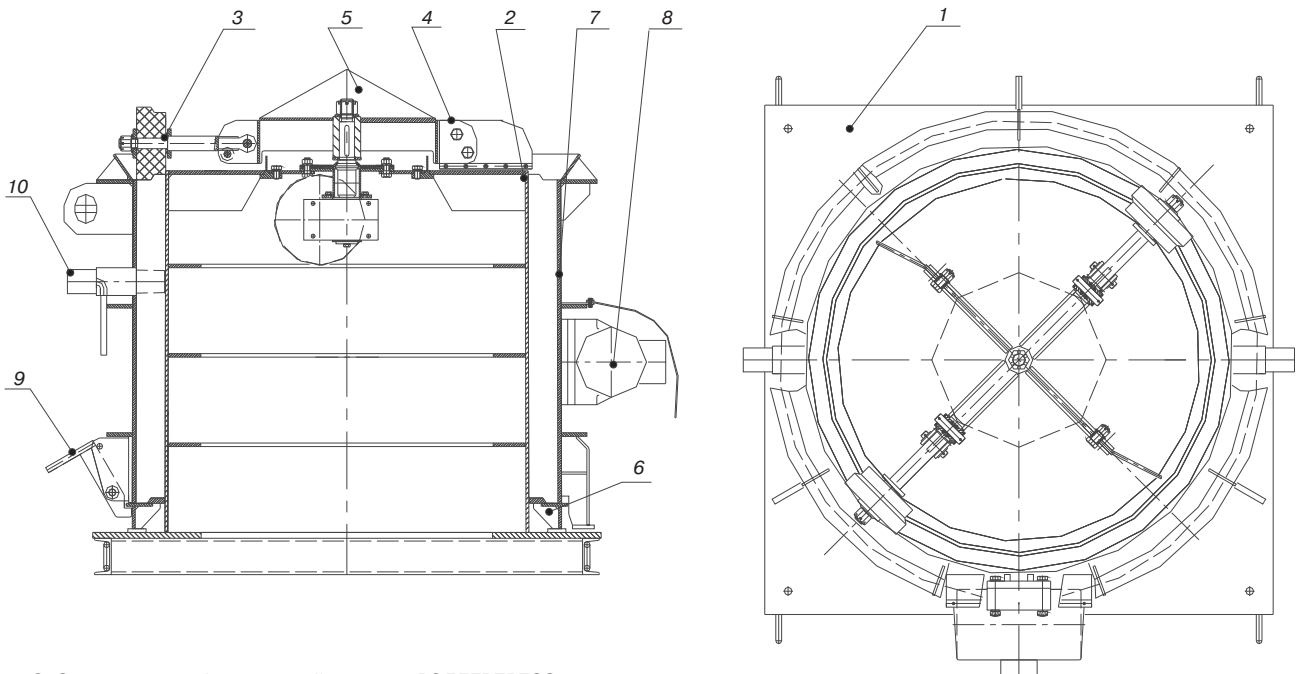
Схема роторно-формовочной машины «РОЛЛЕРПРЕСС»
